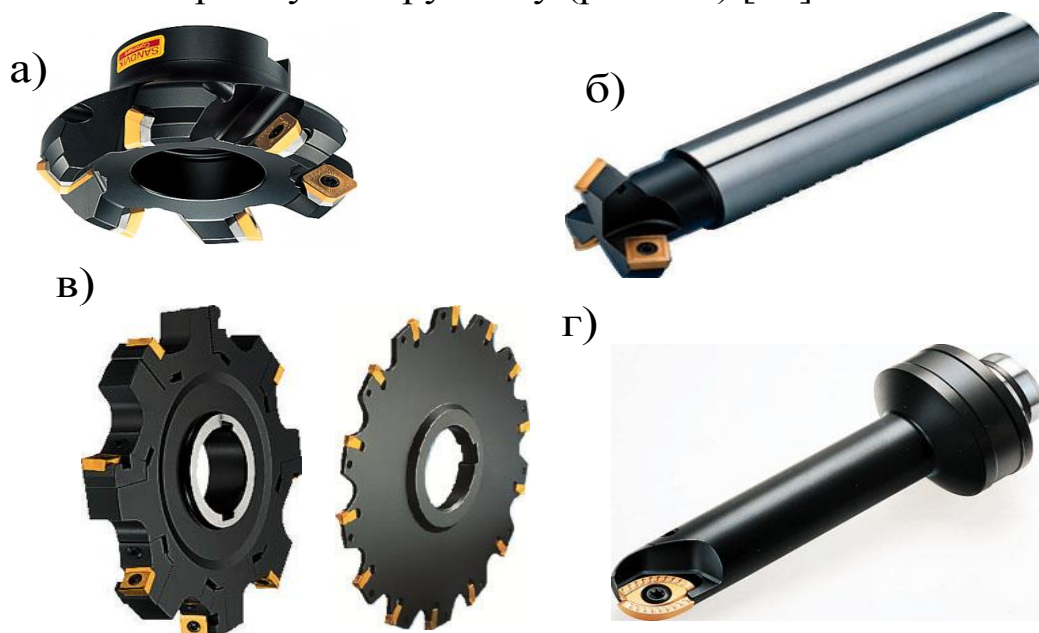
Фотографии сборного инструмента, на примере Sandvik Coromant: а - торцовая фреза; б - дисковые фрезы; в - концевая фреза; г - сферическая фреза
